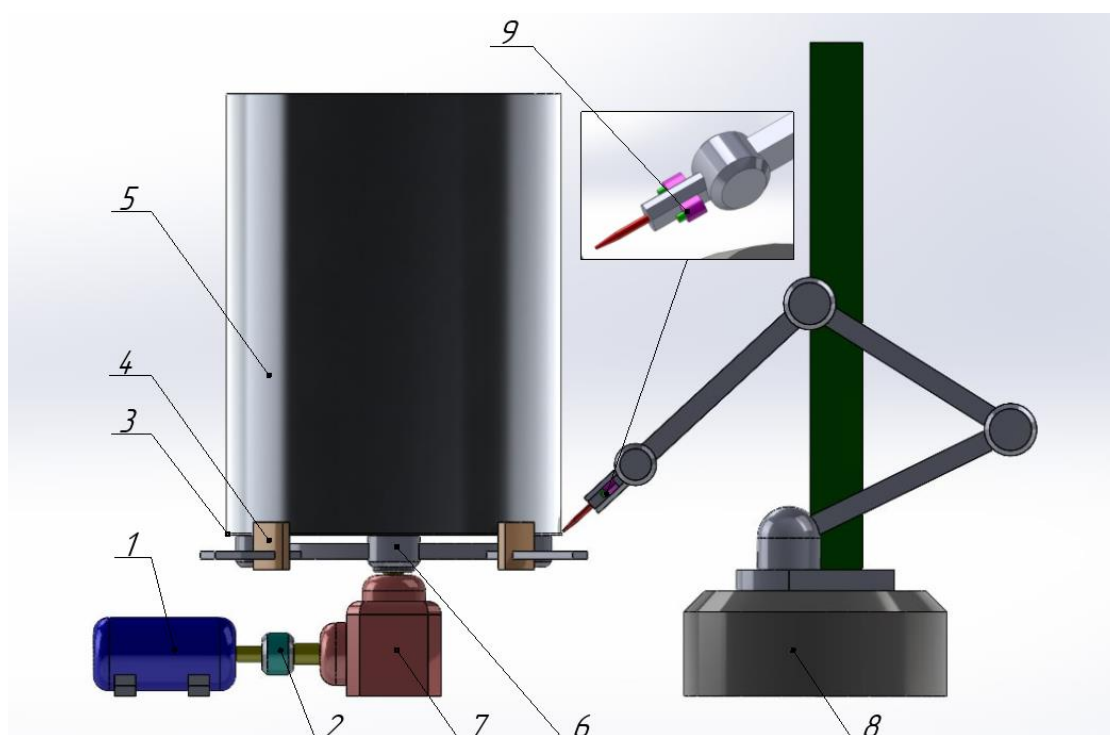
Эскиз автоматизированной технологической установки для сборки цилиндрической оболочки молочного такси (системы ЧПУ и источники питания условно не показаны): 1 – электродвигатель электропривода вращения рабочей платформы, 2 – муфта, 3 – основание рабочего цилиндра, 4 – технологические фиксаторы (изображение представлено в упрощенном виде), 5 – боковая стенка цилиндрической оболочки, 6 – рабочая платформа, 7 – редуктор, 8 – специальный автоматизированный сварочный робот, 9 – датчики параметров технологического процесса сварки
